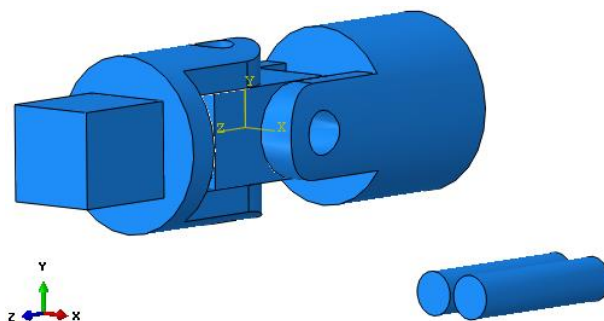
Wybór punktów definiujących oś obrotu elementu *Cardan_2
